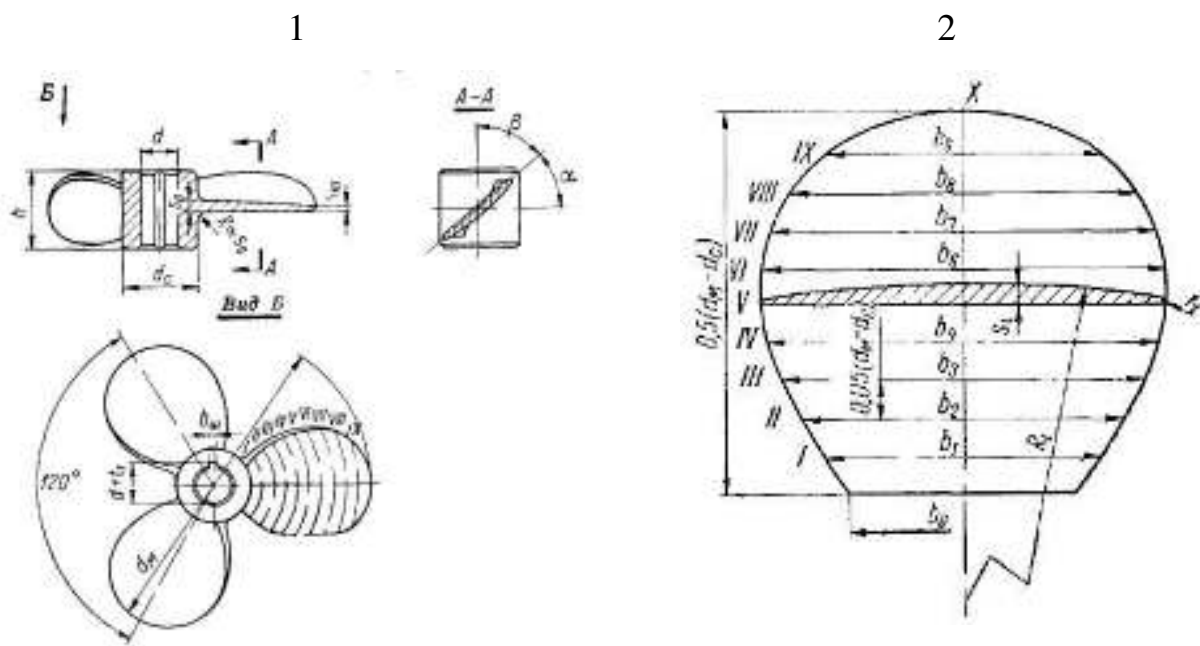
Пропелерний переміщуючий пристрій з профілем криловидної форми [9]: 1 – конструкція; 2 – розгортка лопаті
